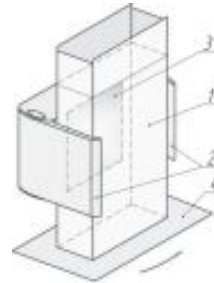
Вертикальний карманний носій з поворотними захватами роторної транспортної системи:
